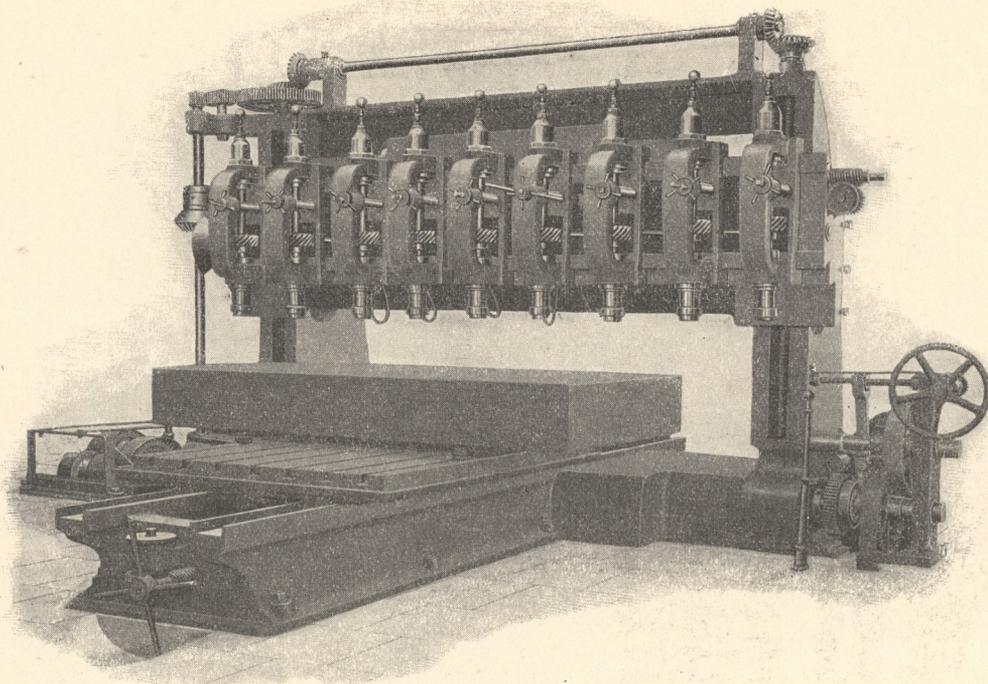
Neunspindlige Bohrmaschine zum Bohren von Wasserkammern.
